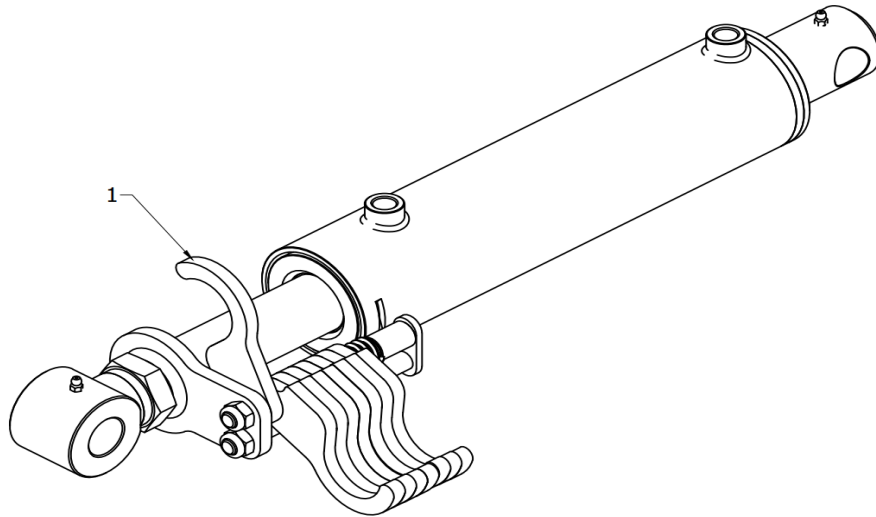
Manière correcte de placer le premier (1) cliquet sur la tige de piston du vérin pour régler la profondeur de travail de la machine.
